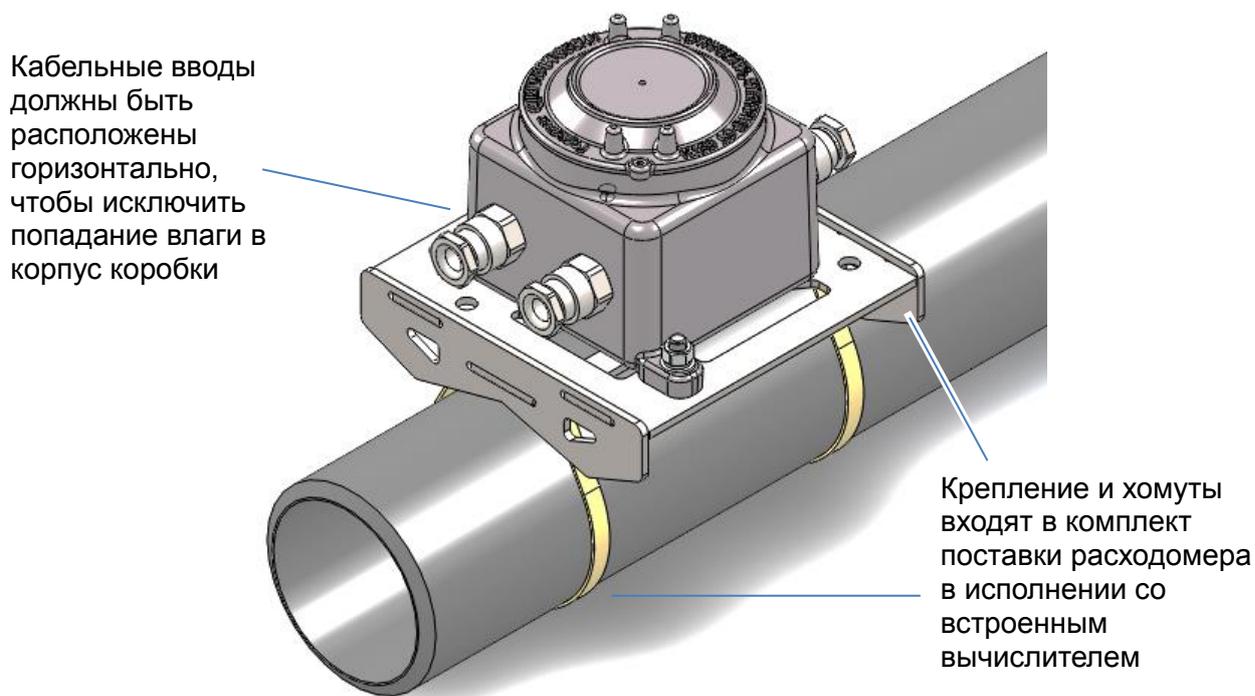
Предлагаемое решение по установке клеммной коробки
